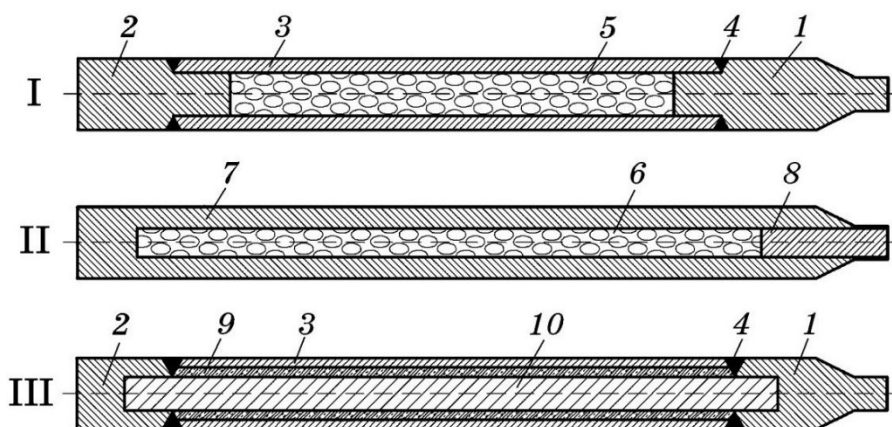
Конструкция заготовок, где 1 – входная часть заготовки, 2 – хвостовик, 3 – тонкостенная труба, 4 – сварной шов, 5 – полость с твердым включением в сварной конструкции, 6 – центральное отверстие в сплошном стержне с твердыми включениями, 7 – сплошной стержень, 8 – заглушка, 9 – алмазные включения, 10 – металлический сердечник [73].
